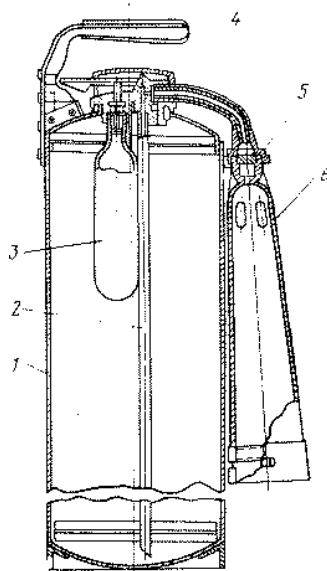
Повітряно-пінний вогнегасник ОВП-10 1 - корпус; 2 - сифонова трубка; 3 - балон; 4 - рукоятка; 5 - розпилювач; 6 - розтруб з сіткою
